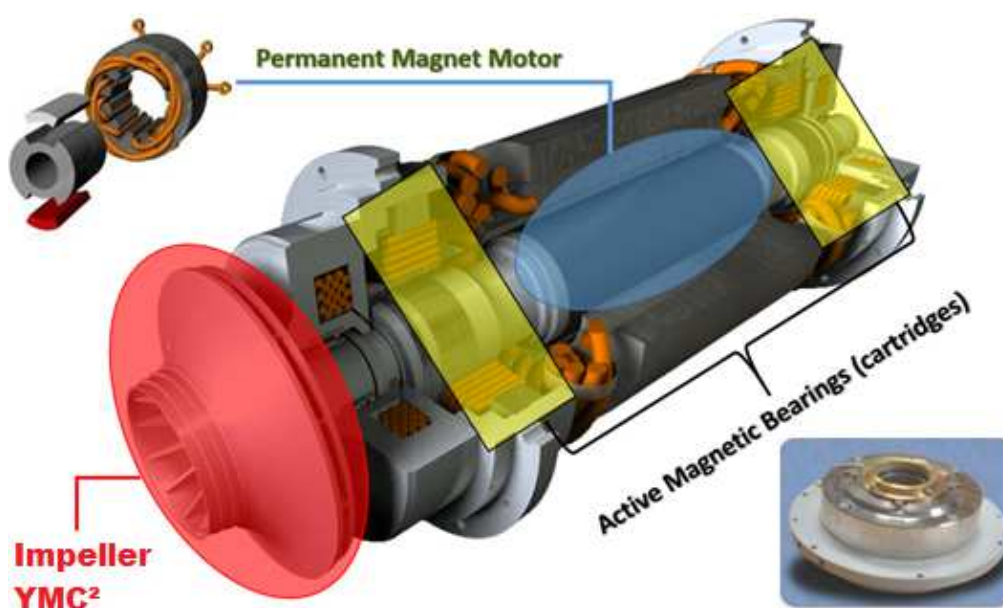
Vista em corte isométrico de um compressor de mancal magnético
